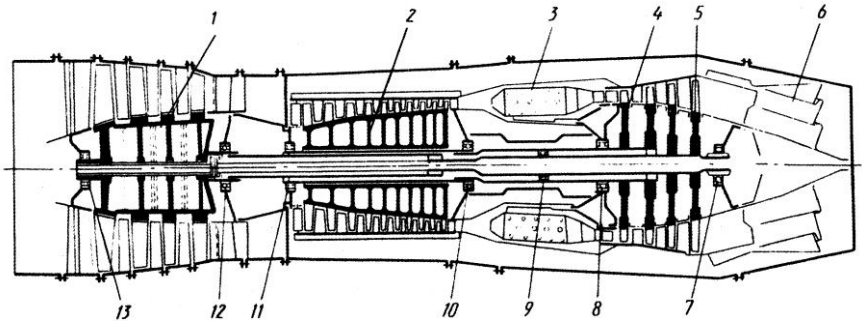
Двухконтурный турбореактивный двигатель со смешением потоков контуров:
